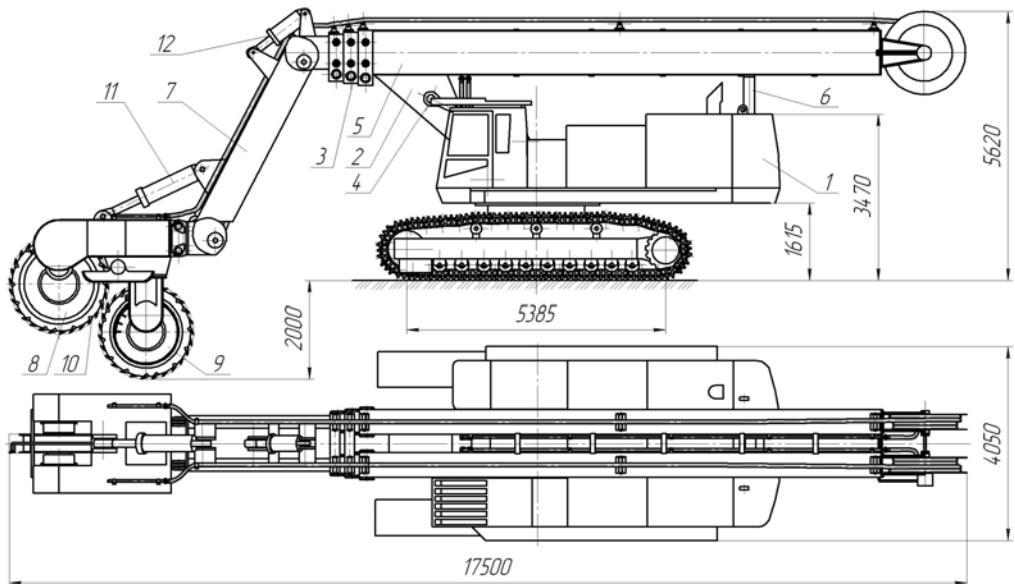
Общий вид дискофрезерного оборудования на одноковшовом экскаваторе Caterpilar 3858L
